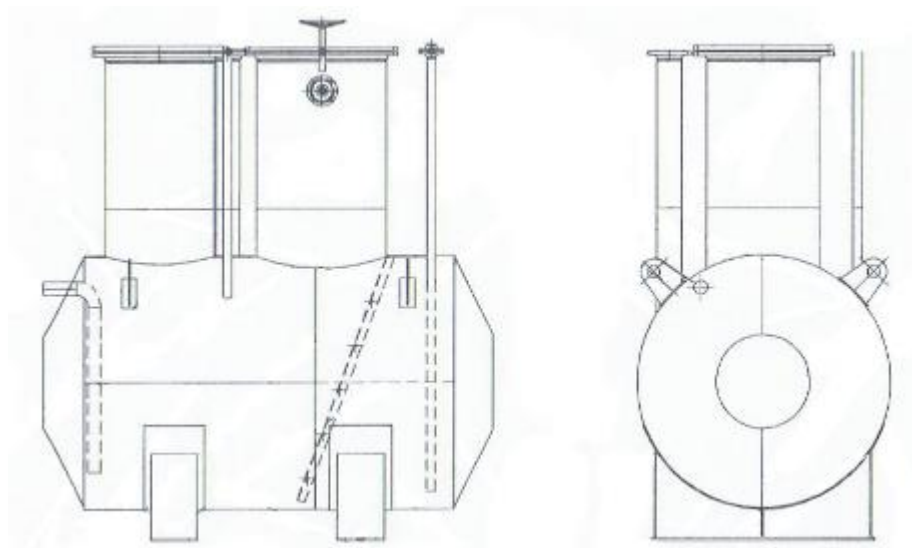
Эскиз общего вида резервуара ЕП-16-2000-1300
